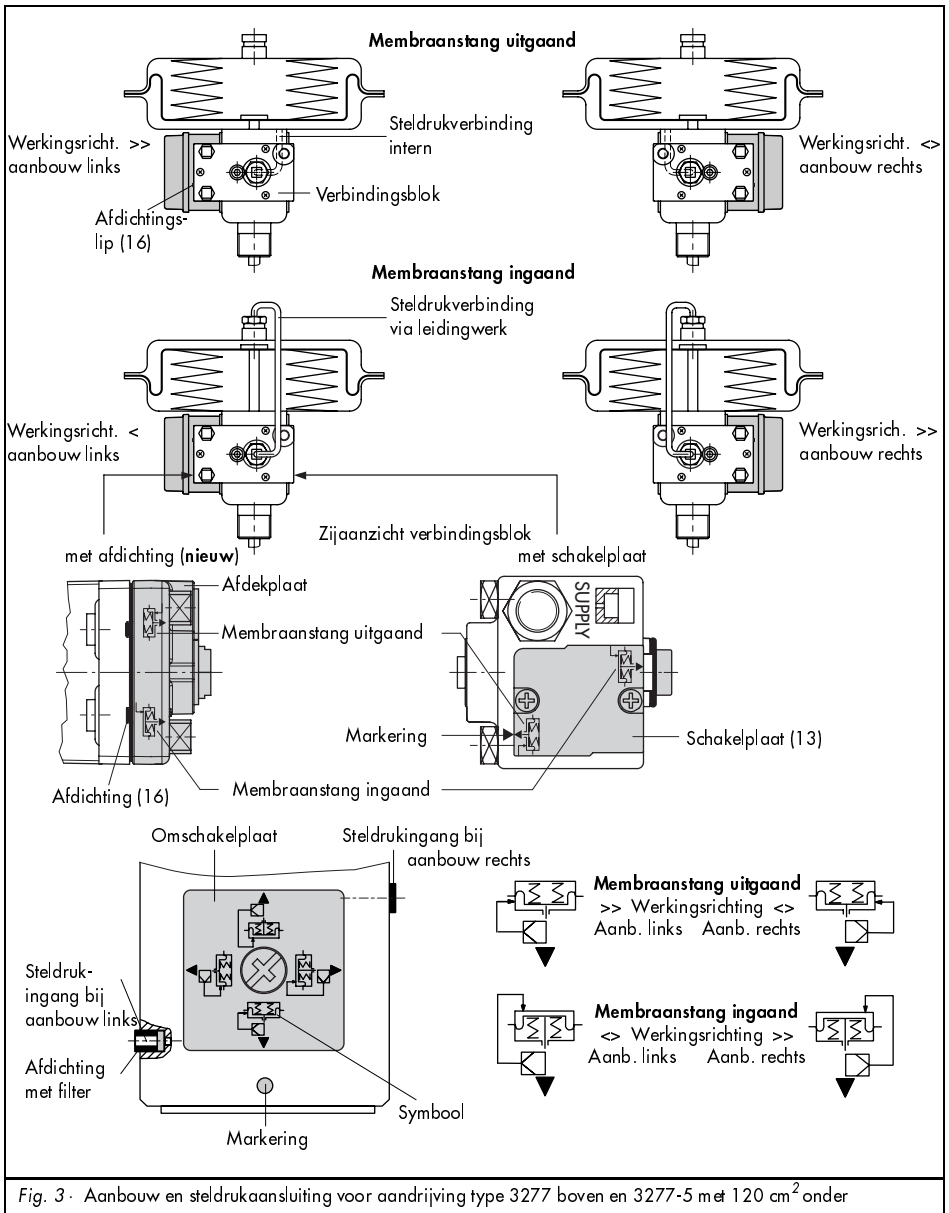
Aanbouw en steldrukaansluiting voor aandrijving type 3277 boven en 3277-5 met 120 cm<sup>2</sup> onder
